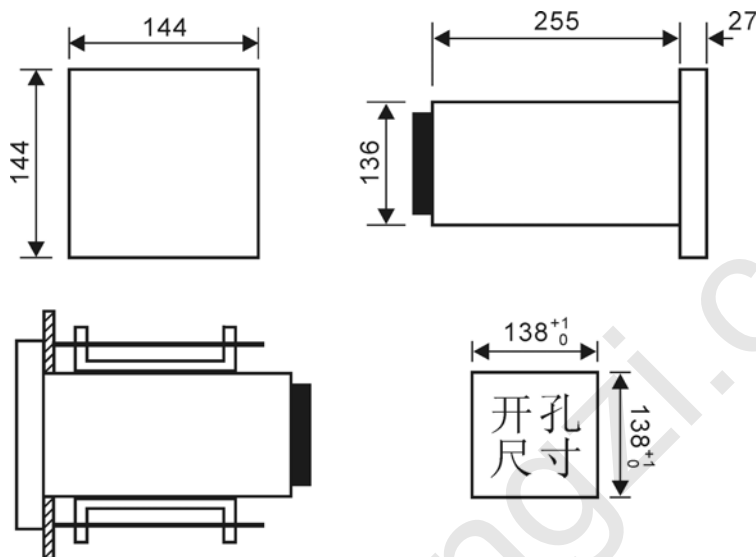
仪表外形尺寸，安装方法及开孔尺寸
